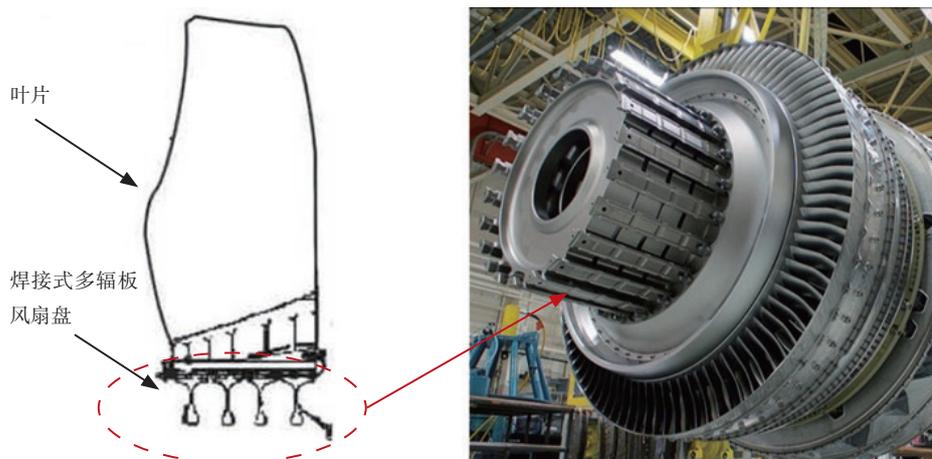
惯性摩擦焊接的GE90-115B风扇盘组件
